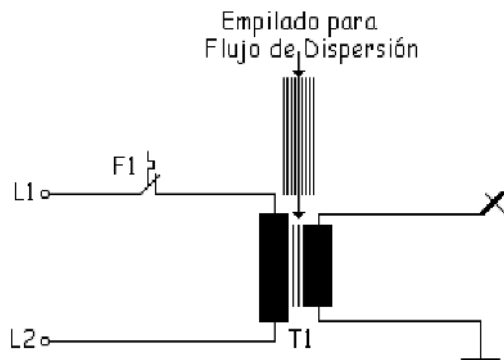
Esquema de soldadura con regulación por flujo de dispersión.
